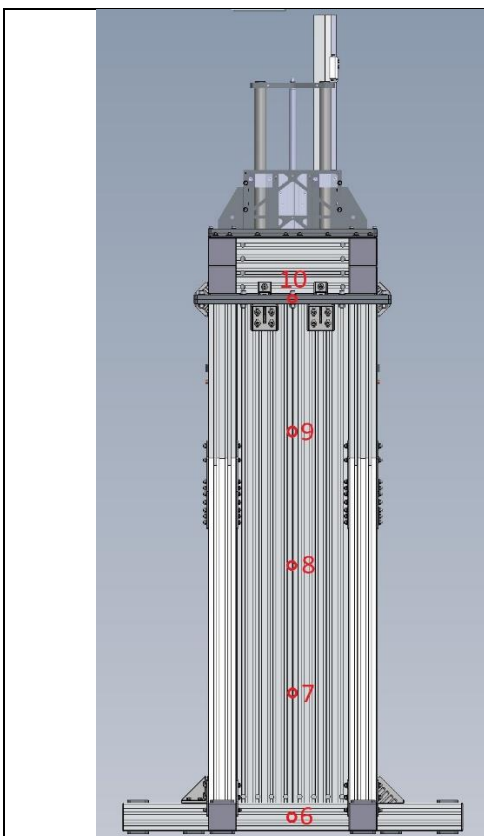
Posiciones vista izquierda. Fuente: Elaboración Propia
